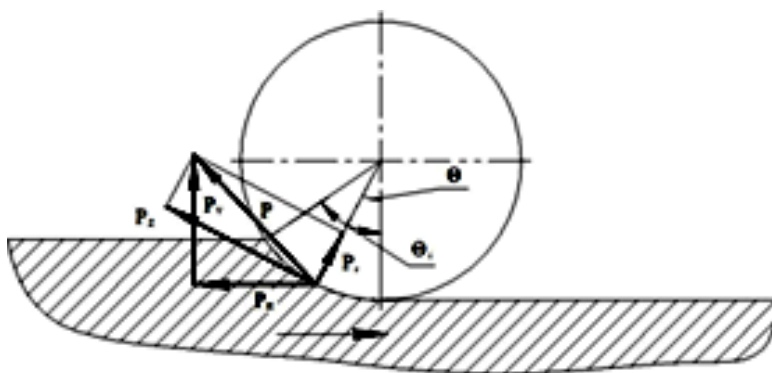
Схема силового взаимодействия концевой фрезы и заготовки при плоском контурном встречном фрезеровании приложены в некоторой точке, определяемой значением центрального угла  $\Theta_i$
